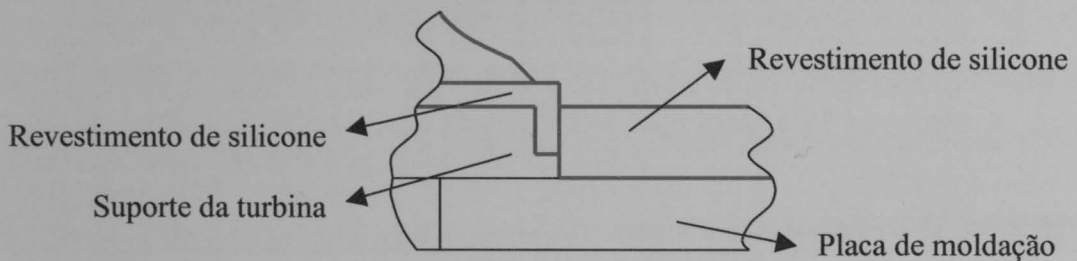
5 - Pormenor do encaixe dos impulsores de silicone na placa molde.
